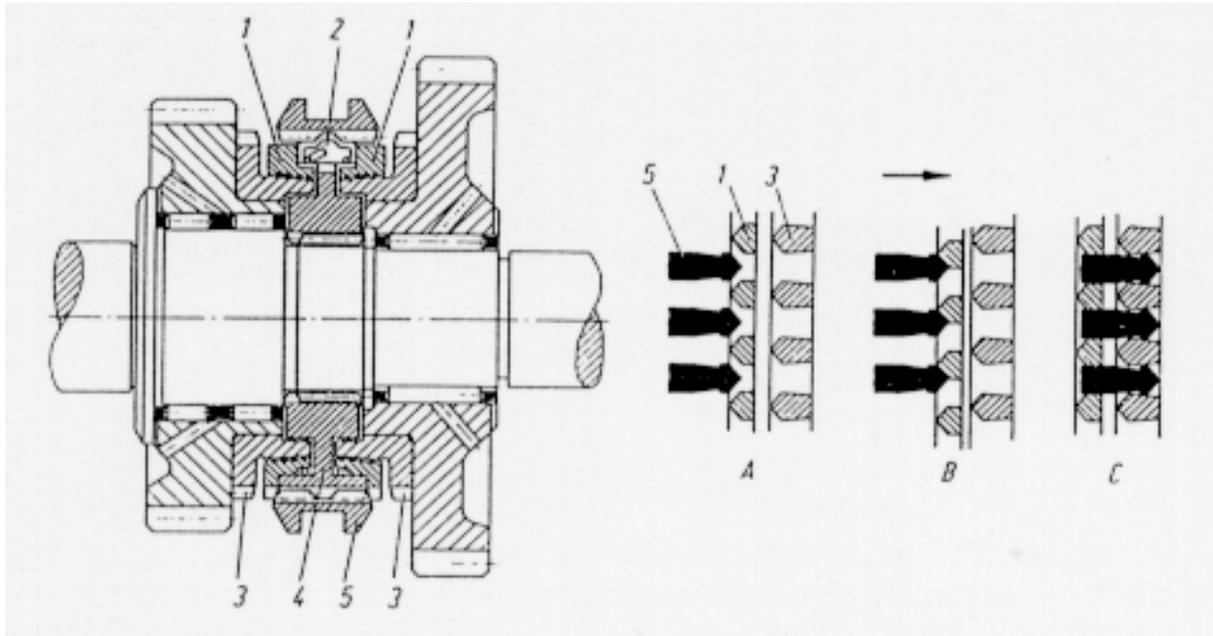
Kraftfahrzeug-Sperrsynchonisierung (Zahnradfabrik Friedrichshafen AG)
